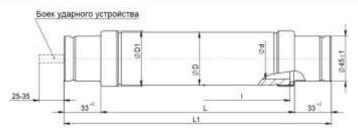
Габаритные, присоединительные и установочные размеры патронов.
